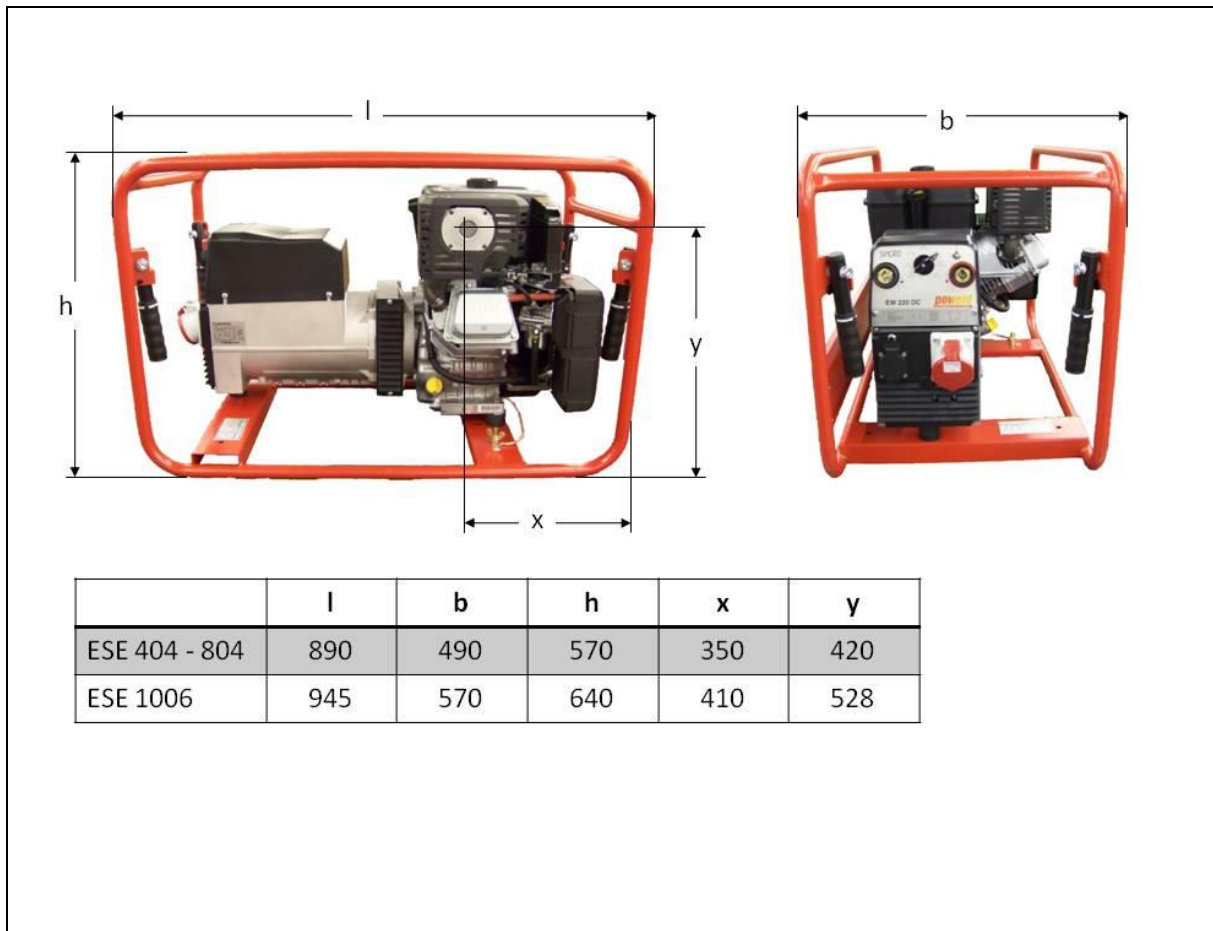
Maße des Schweißstromerzeugers
